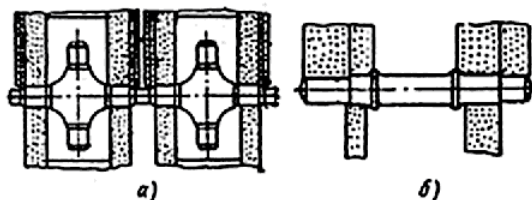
Схемы многокруговых наладок при обработке разобщенных поверхностей: а – шипов крестовины; б – ступенчатого вала
